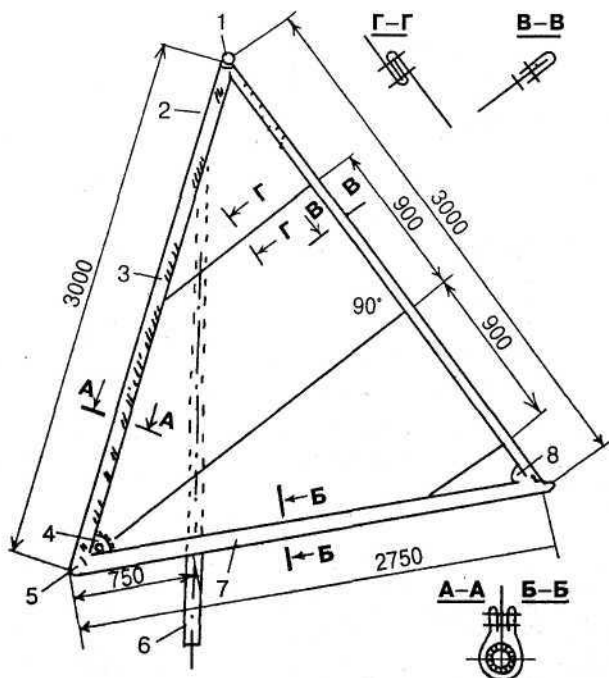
Парусное вооружение швербота: 1 — гафель; 2 — косынка фалового угла паруса с люверсом; 3 — карман; 4 — косынка галсового угла с люверсом; 5 — гик; 6 — мачта; 7 — карман; 8 — косынка шкотового угла с люверсом
